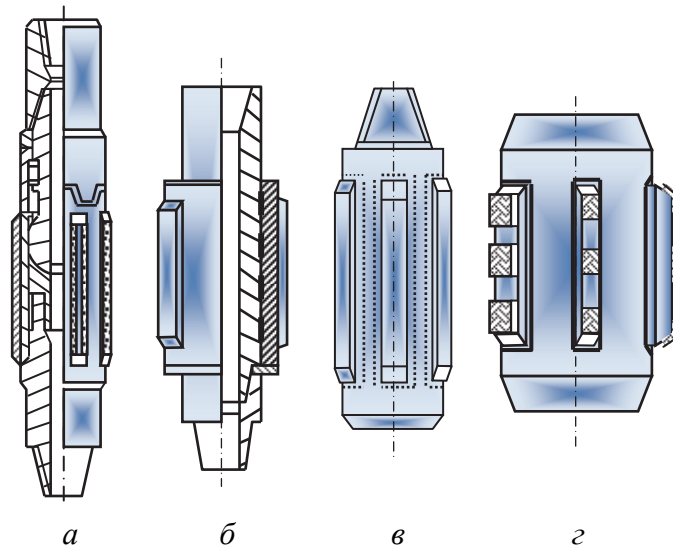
Конструкции центраторов для КНБК: *а* – с буровым шарниром; *б* – с вращающимся корпусом; *в, г* – лопастные
